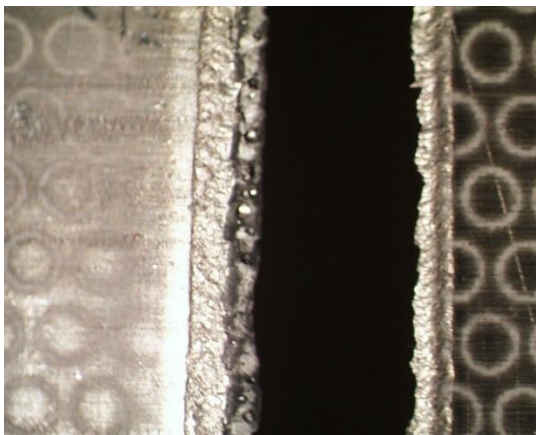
Visualização de poros na zona do cordão de soldadura.
